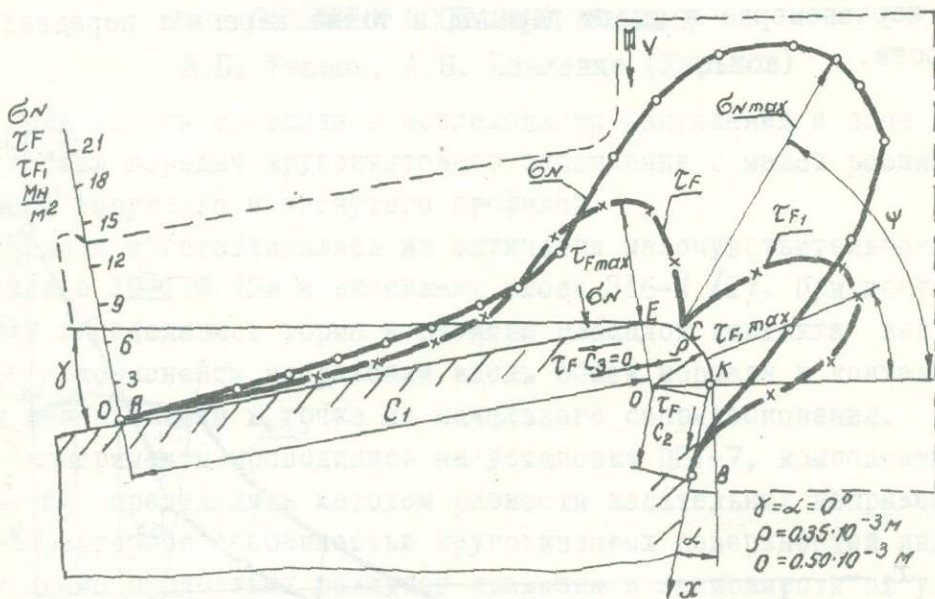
Рис. I. Контактные напряжения на резце с округленной режущей кромкой
